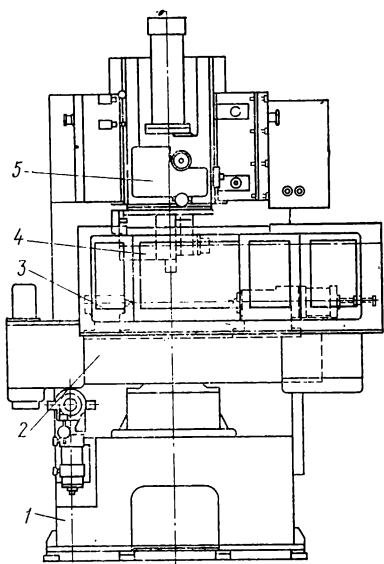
Общий вид зубошевинговального станка с вертикальной подачей вниз головки шевера
